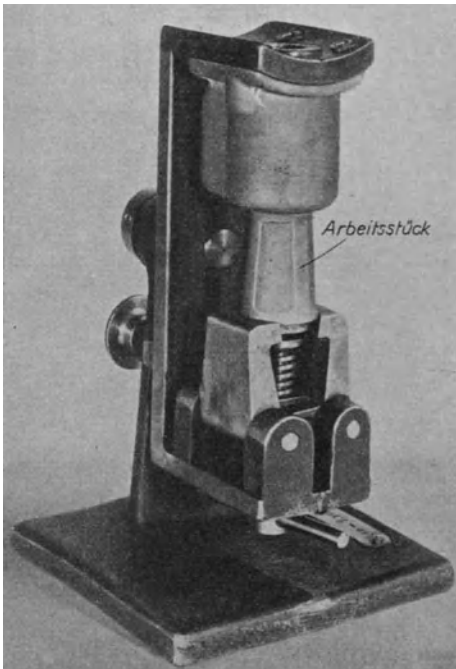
Schwenkbare Bohrvorrichtung für die Handgriffe zur elektrischen Handbohrmaschine.
